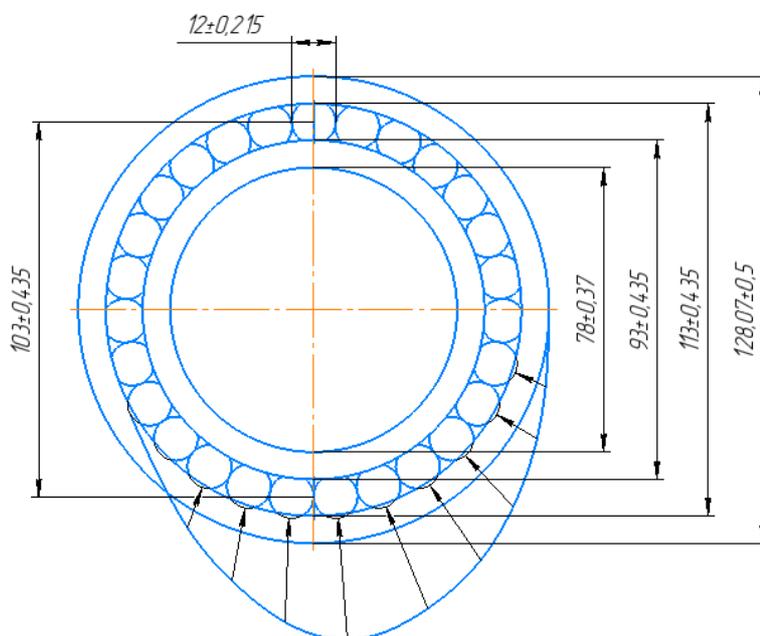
Фронтальный вид специального бессепараторного подшипника
